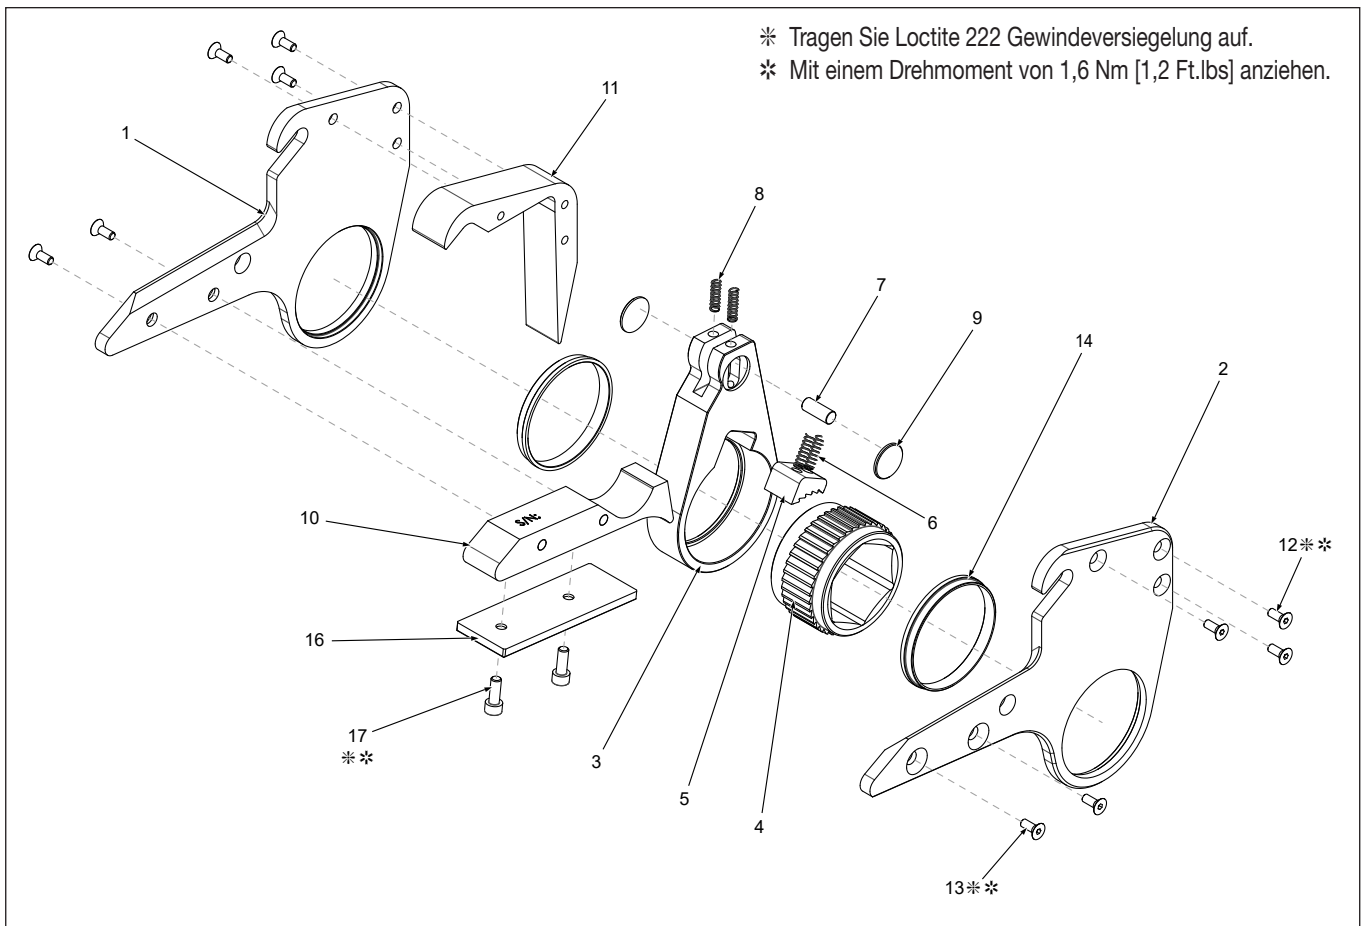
Explosionsansicht HMT HLP-Kassette
